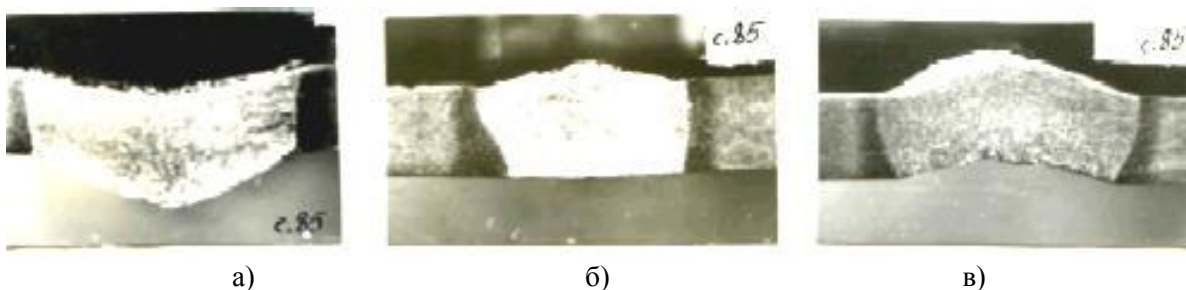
Макрошлифы швов, выполненных при разной величине индукции магнитного поля в сварочной ванне [Macroscale stitches made at different values of magnetic field induction in the weld pool]:
